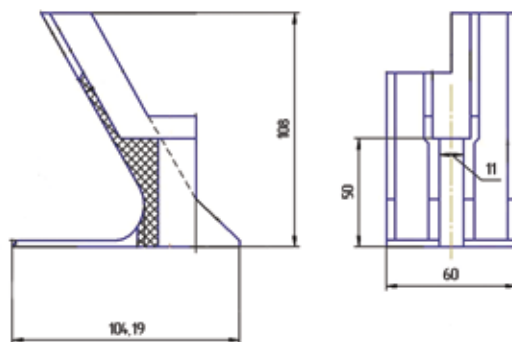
Внешний вид и габаритные размеры УКК-60 (мм)
